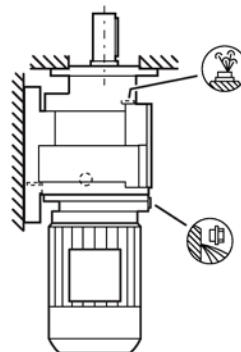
Монтажные положения для цилиндрического редуктора D/Z в исполнении на лапах, типоразмеры 39-189
